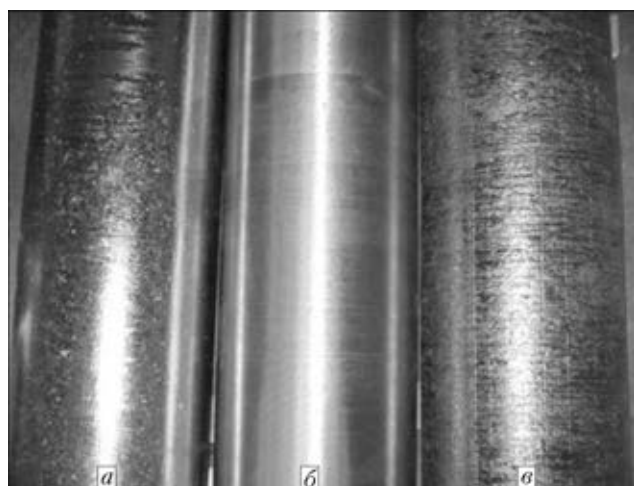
Внешний вид поверхности слитков титана: а — оплавленной; б — механически обработанной; в — литой слиток
